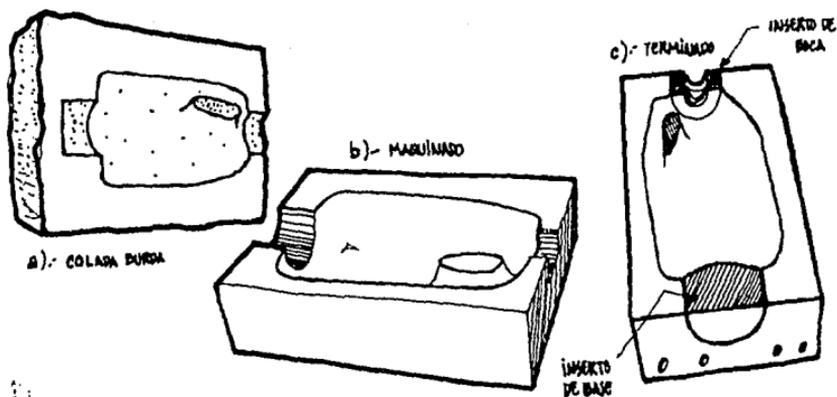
Estaciones de la fabricación de un molde de extrusión-soplo a).-Colada burda b).- Maquinado y, c).- Acabado
